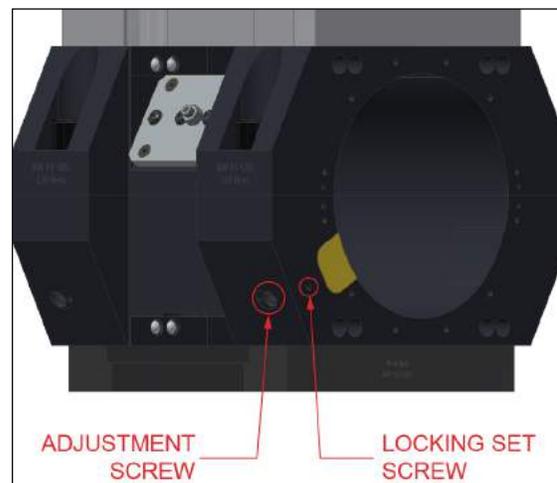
Einstell- und Stellschrauben im Werkzeugträger
